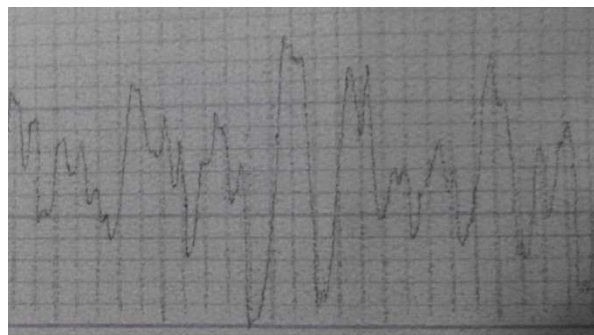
Профілограма обробленої поверхні циліндричного вала
